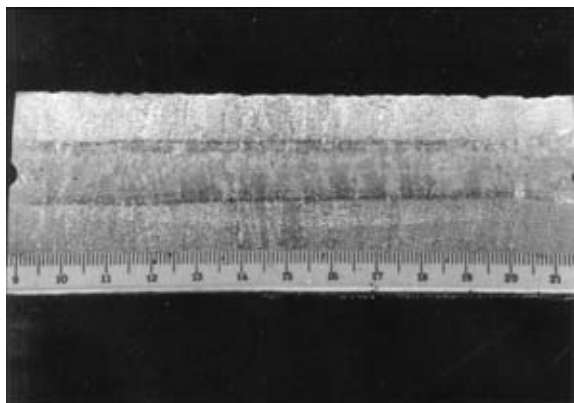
Макрошлиф стыкового сварного соединения сплава ВТ6 толщиной 120 мм, выполненного ЭЛС горизонтальным лучом
